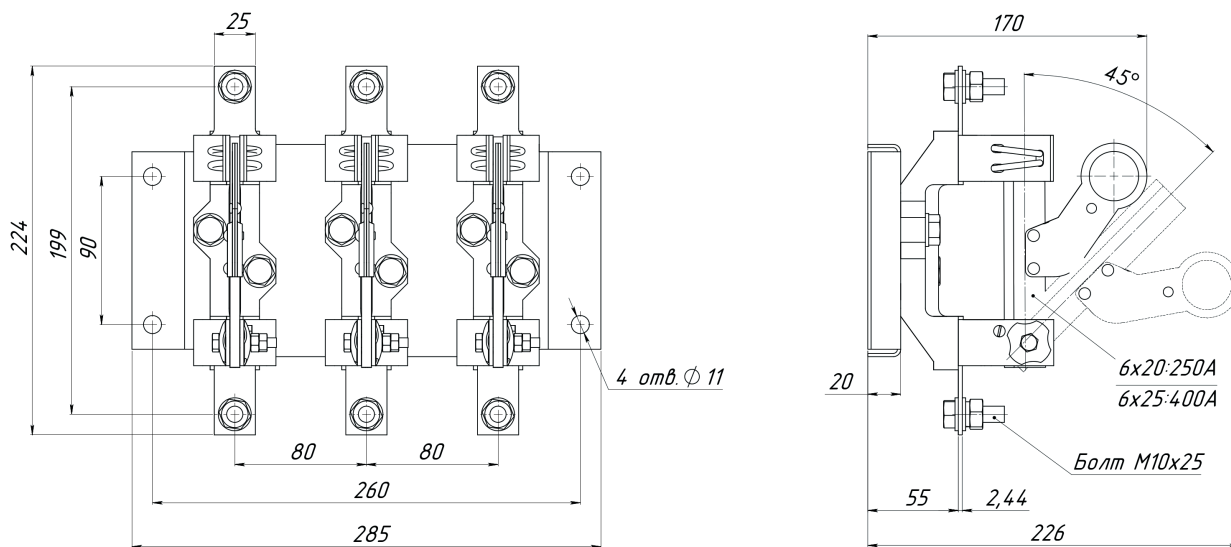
Разъединитель серии Р с полюсным оперированием штангой Р 43, на номинальный ток 250 А и 400 А
